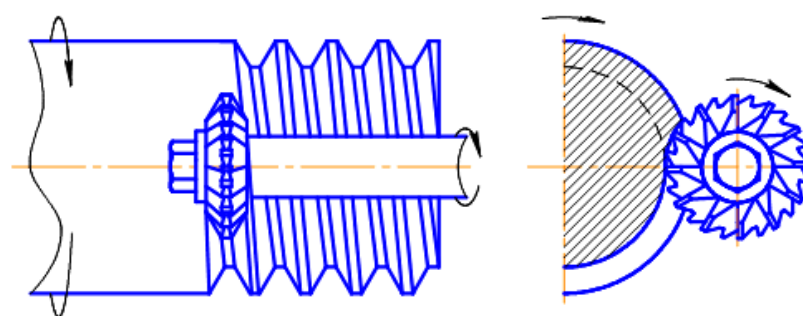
Схема фрезерования наружной резьбы дисковой профильной фрезой
